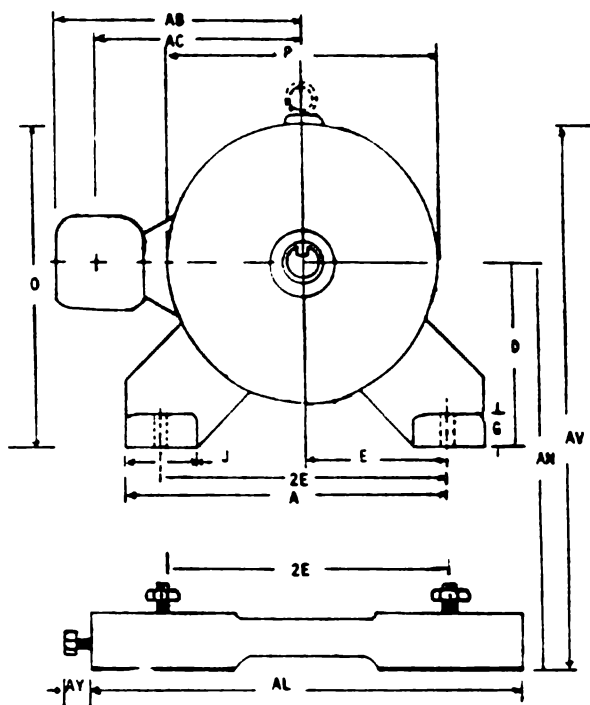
DIMENSIONAMIENTO POR LETRAS PARA MAQUINAS MONTADAS AL PISO, VISTA FRONTAL.
